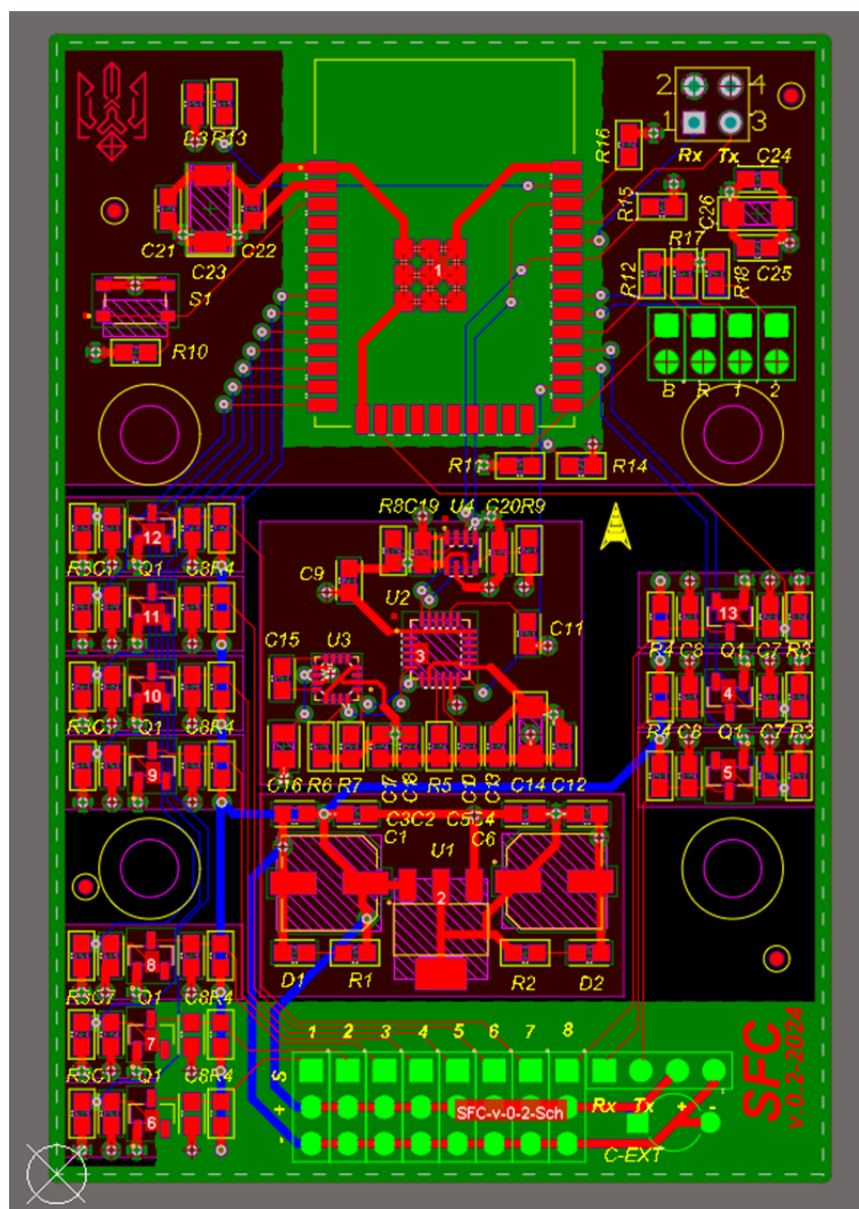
Зовнішній вигляд шарів друкованої плати в вікні редактора PCB Editor Altium Designer.
